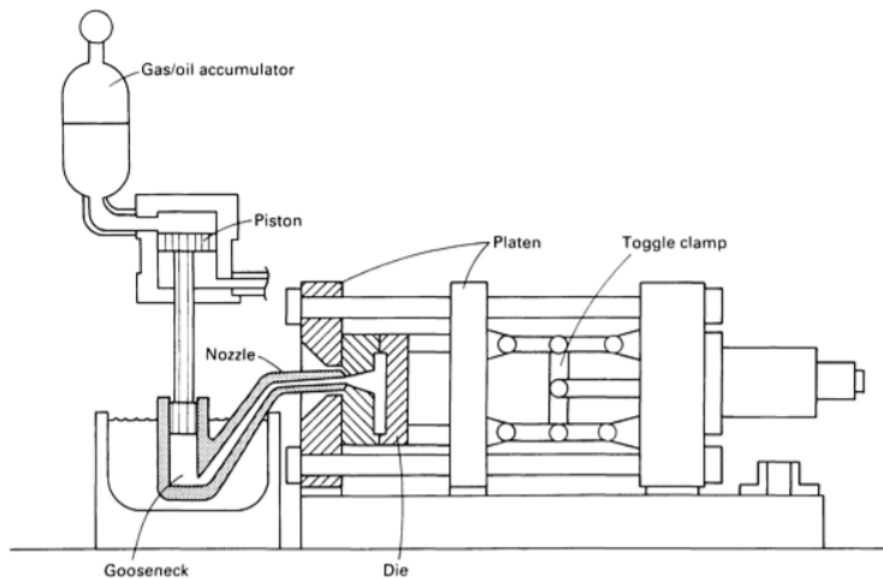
Machine à chambre chaude [BUTLER (2008)]
